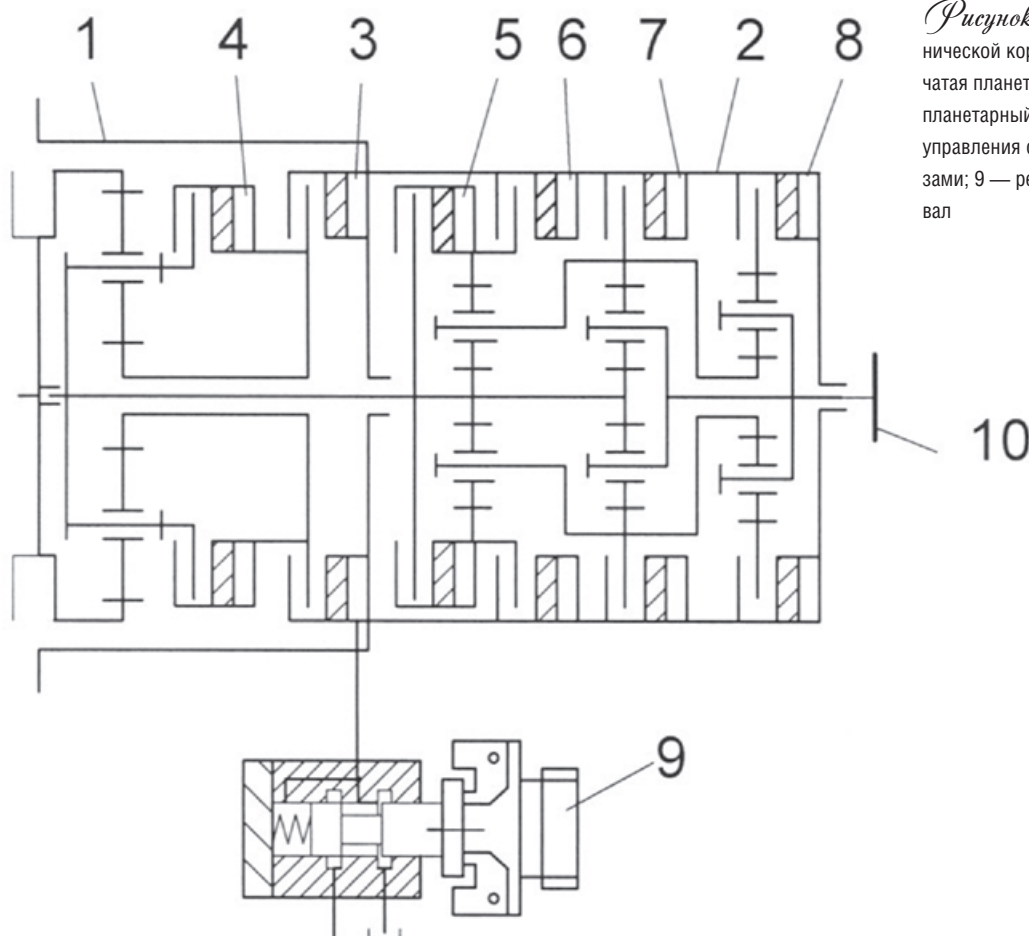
Кинематическая схема механической коробки передач: 1 — двухступенчатая планетарная передача; 2 — ступенчатый планетарный редуктор; 3–8 — цилиндры управления фрикционными муфтами и тормозами; 9 — регулятор давления; 10 — выходной вал
